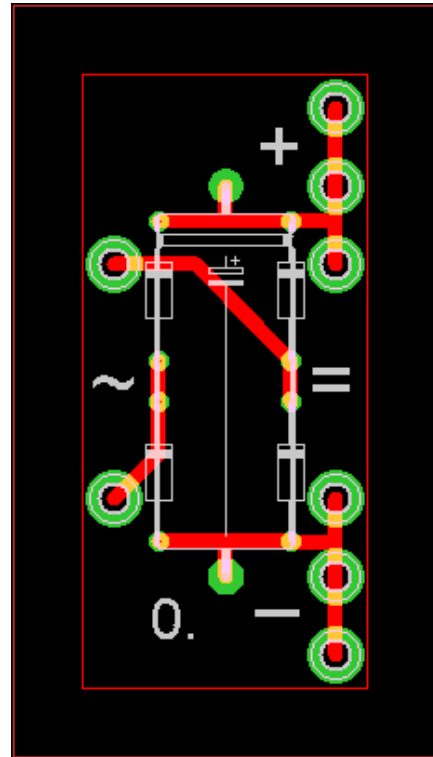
Nachbau 4: Platinenentwurf für das Batteriegehäuse ([32263](#))
